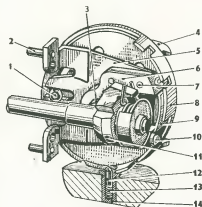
Механизм переключения передач: 1 — ось вилки; 2 — установочный штифт; 3 — ось корпуса собачки; 4 — вилка; 5 — основание механизма; 6 — корпус собачки; 7 — стопорный штифт; 8 — диск; 9 — утопитель собачки; 10 — собачка; 11 — поводок валика; 12 — корпус фиксатора; 13 — пружина; 14 — фиксатор.
